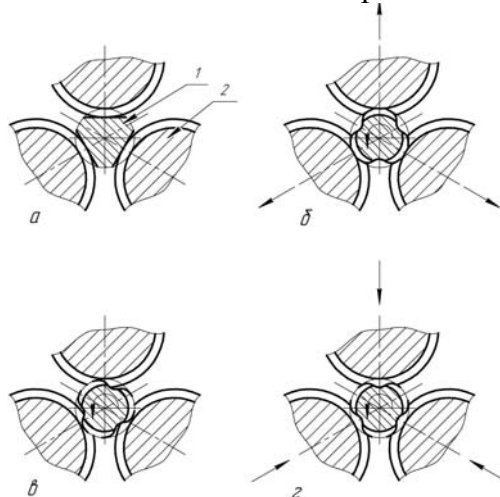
Схема (авт. свид. SU 1065069) получения затылованного резьбового профиля на метчике: а – исходное состояние заготовки и резьбонакатных роликов; б – вращение заготовки и согласованное продольное перемещение резьбонакатной головки к вершинам граней; в –
